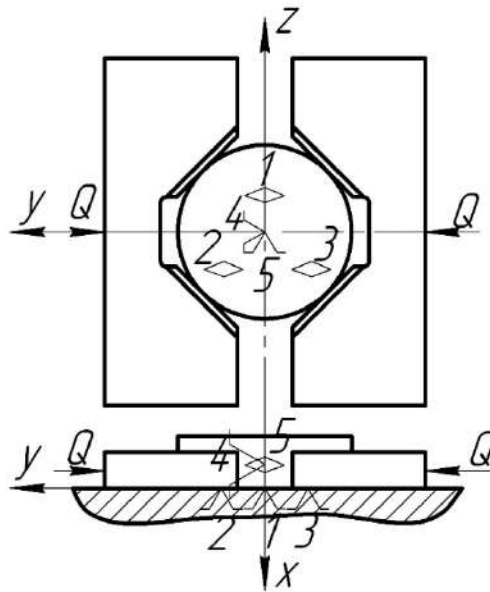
Базування циліндричної заготовки на площину і центрування двома призмами, що сходяться.
